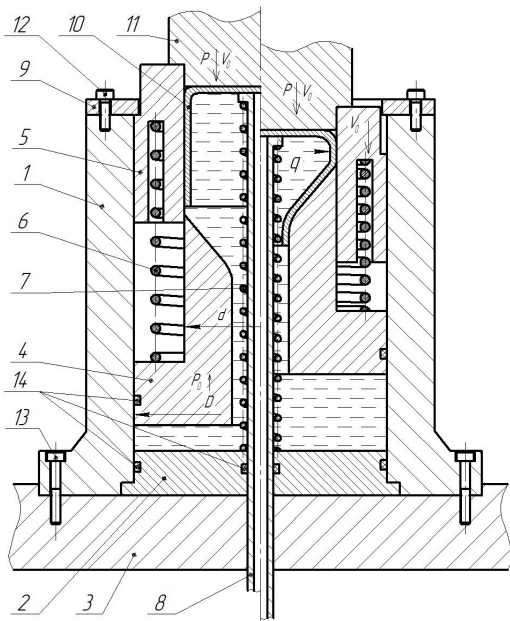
Схема штампу для обтиску в умовах дії диференційованого протитиску на стінки заготовки
